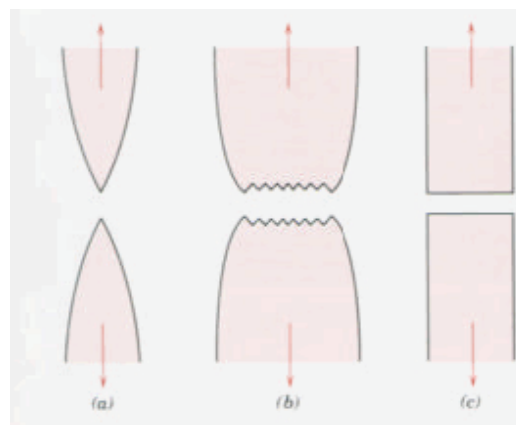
Esquema de una fractura dúctil (a), fractura moderadamente dúctil (b) y fractura frágil sin deformación plástica (c)
